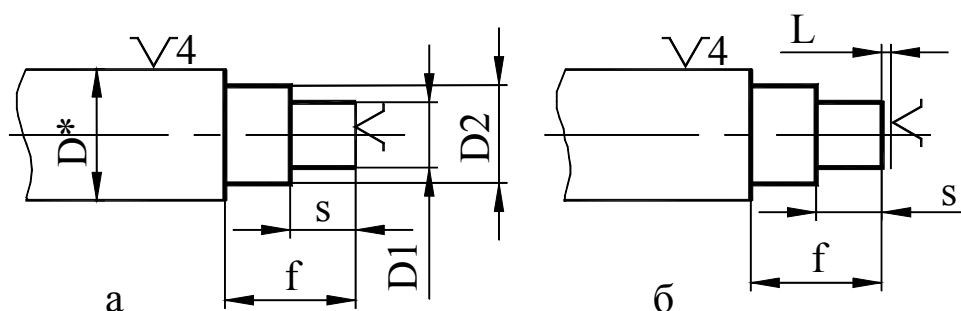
Базирование прутка на токарном станке: а – без подрезки торца; б – с подрезкой торца; L – ширина подрезки торца, s , f – операционные размеры
